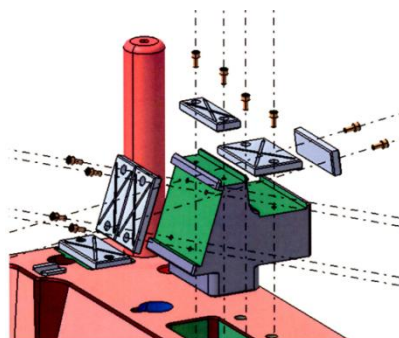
Colocação das placas de travamento e ajuste do molde no lado fixo.
